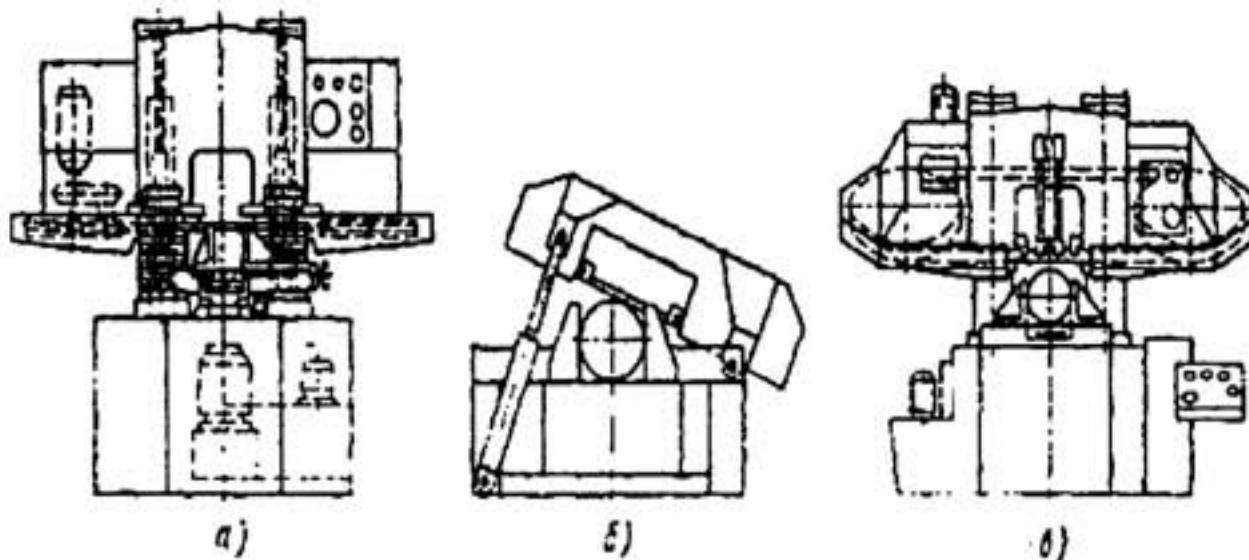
Станок с горизонтальным движением ленточной пилы:
